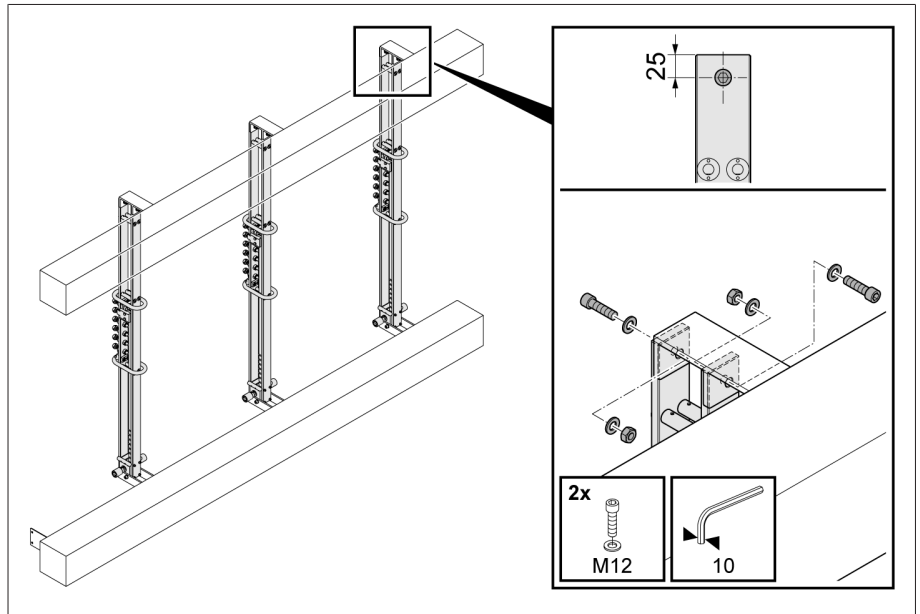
Tragstab befestigen, Umsteller mit frontal angebrachten Kontakten
